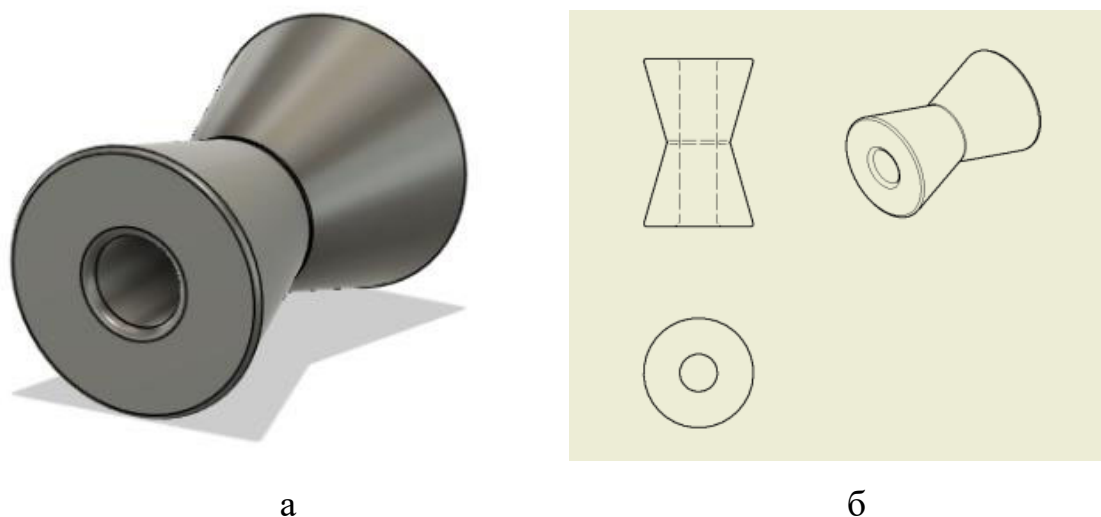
Модель та креслення валку із пластику UHMW Black
